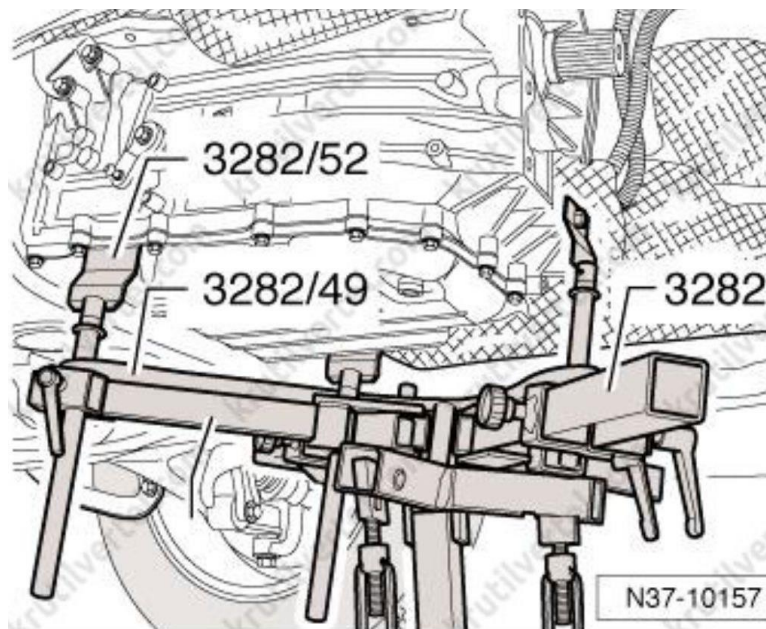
Пристрій для закріплення коробки 3282
